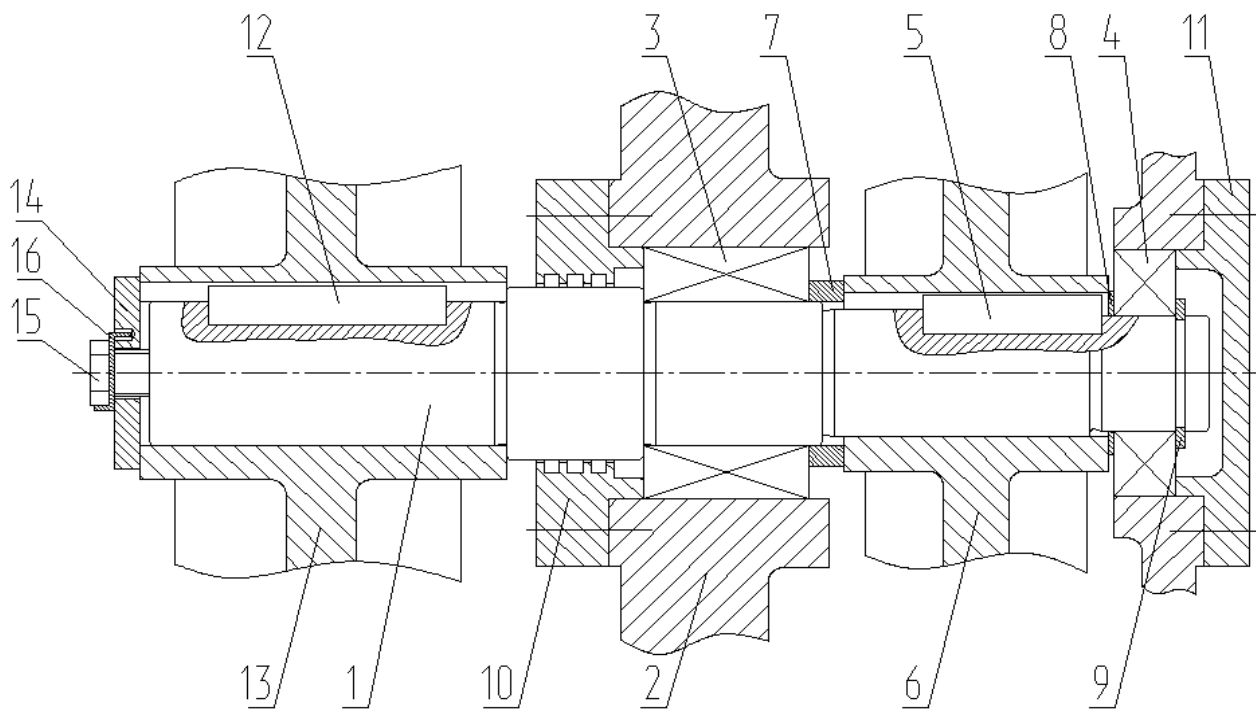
Фрагмент узла мотор-редуктора
